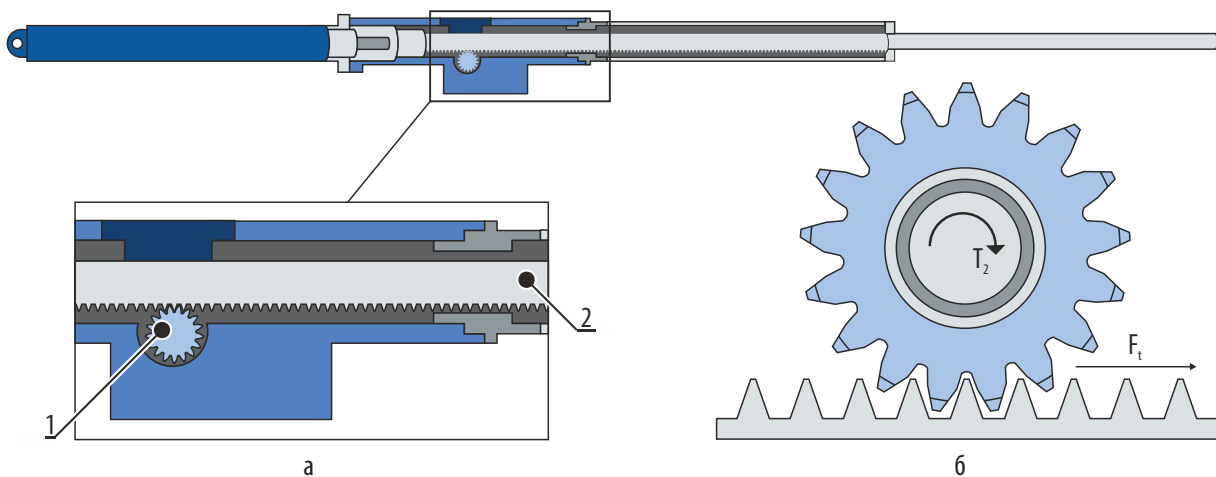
Общий вид (а) и схема (б) реечного механизма приводов рабочих органов аварийной защиты, компенсации реактивности и автоматического регулирования реактора РБТ-10/2: 1 — колесо; 2 — рейка
